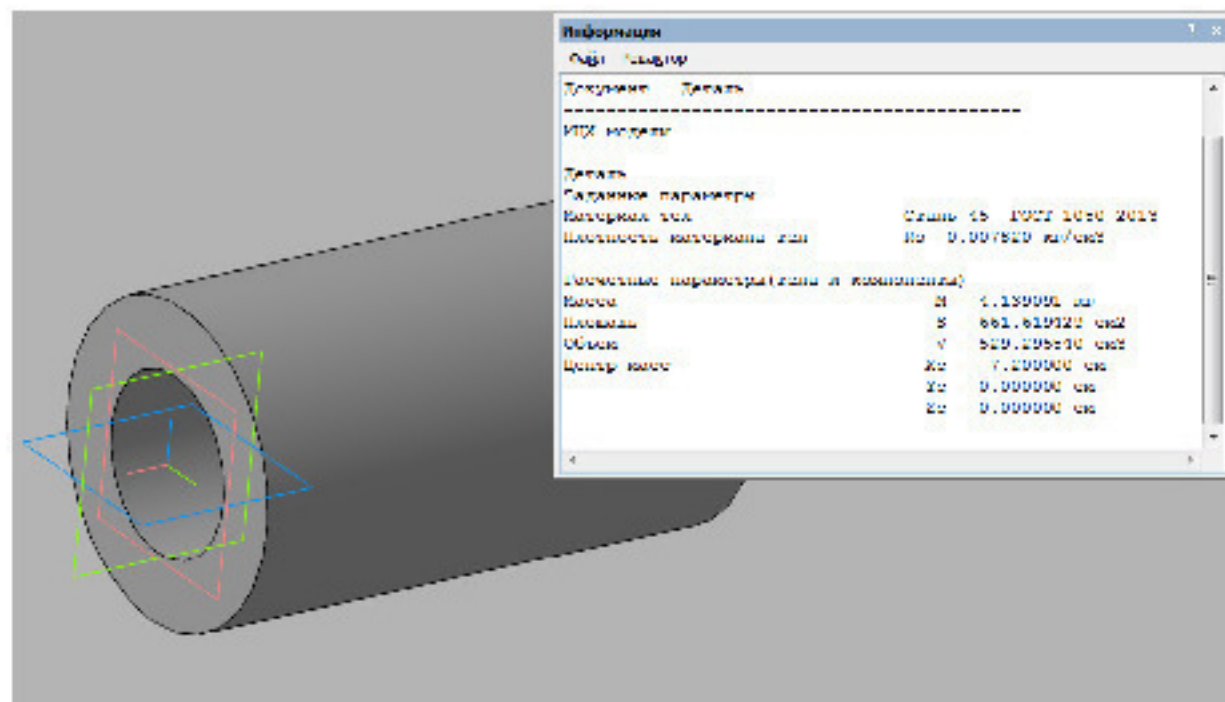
3D-модель заготовки виготовленої трубним прокатом
